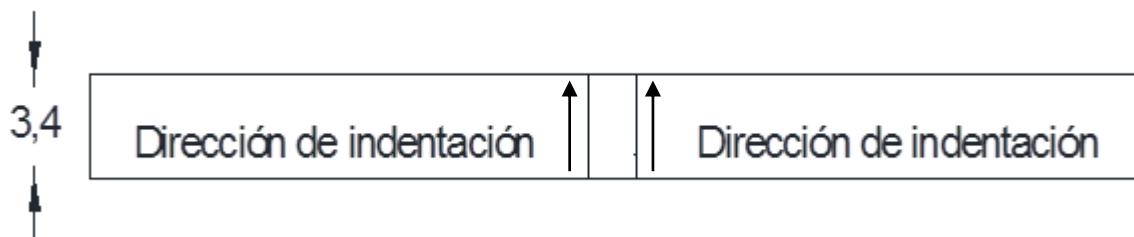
Sección de indentado en la cara de la soldadura para la unión A.
